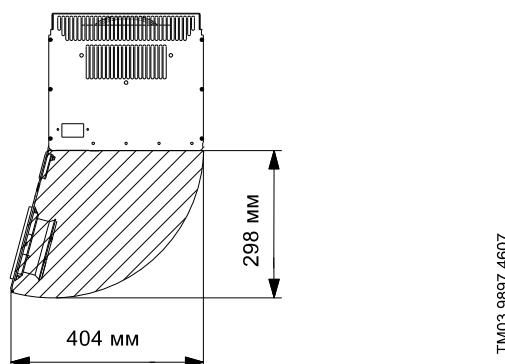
Свободное пространство перед CUE, корпус D1h и D2h
